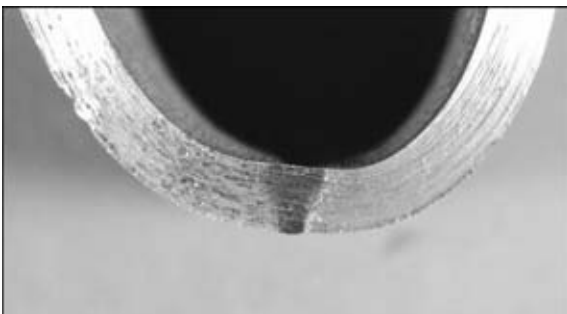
Вид сварного образца из материала толщиной 4 мм после испытаний на загиб
